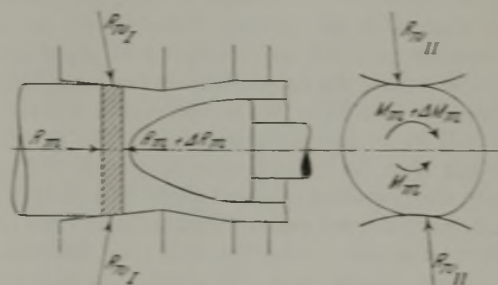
Kräftegleichgewicht im ersten Walzabschnitt.
